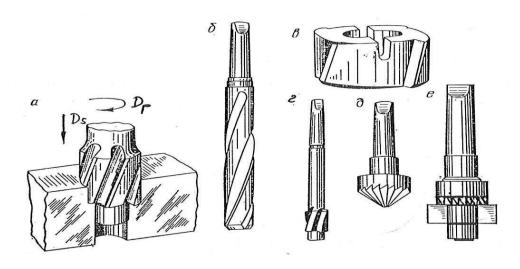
Инструмент для работы на сверлильных станках: а – резание при зенкеровании; б – трехзубый зенкер; в – насадной зенкер; г, д – зенковка; е – цековка
